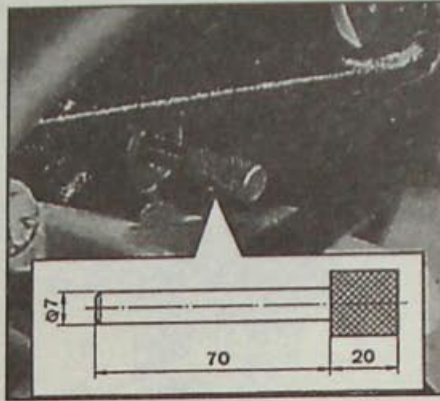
Место установки и размеры приспособлением Mot. 1318 для блокирования коленчатого вала
